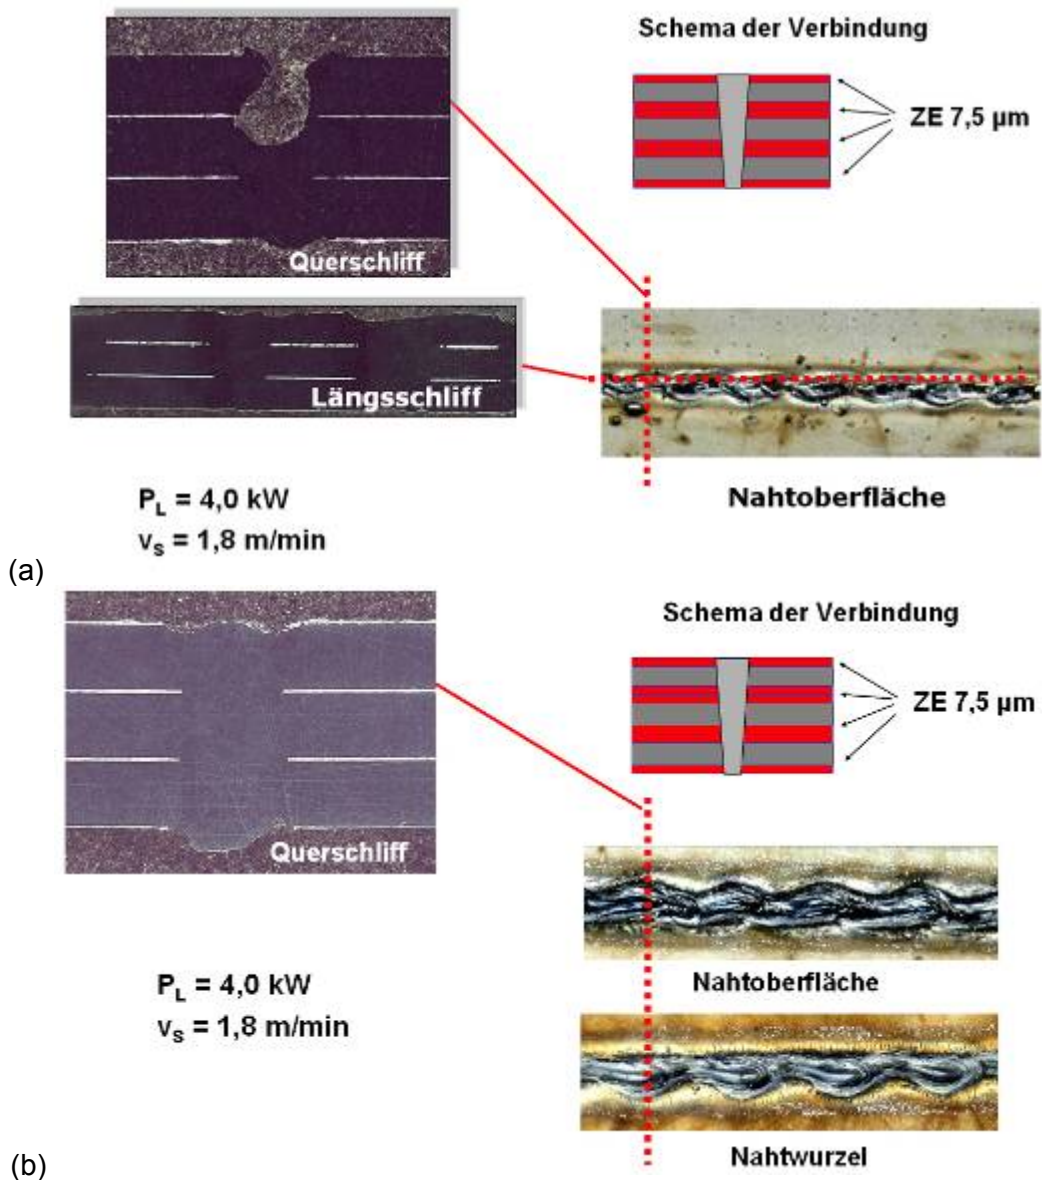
Einsatz der rotierenden Optik an ZE-beschichteten Blechen (Werkstoff: DC04+ZE 75/75);
